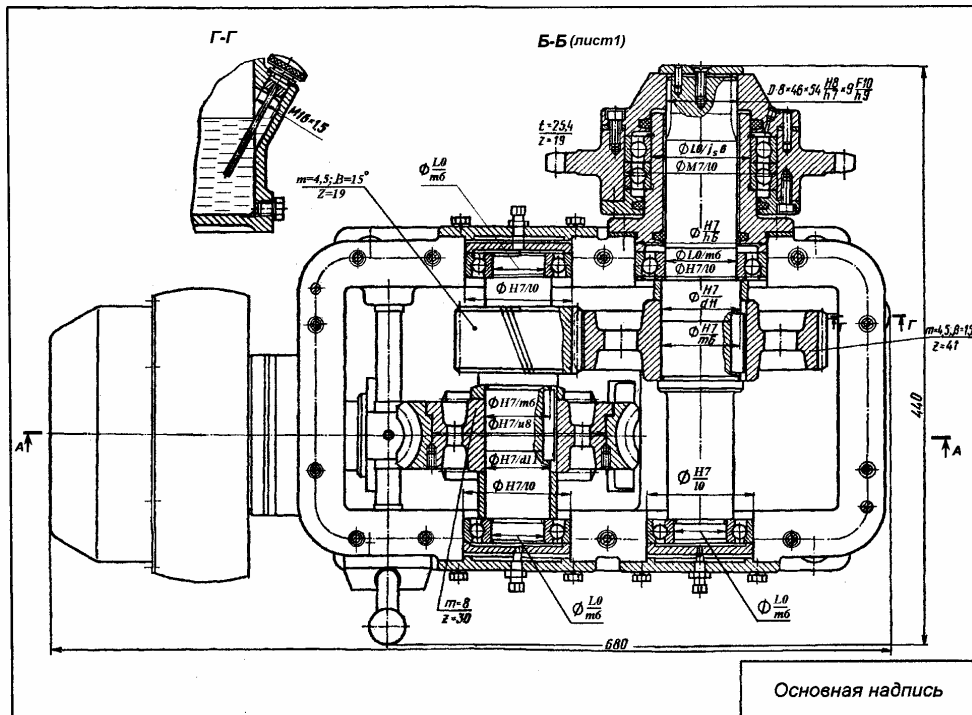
Редуктор червячно-цилиндрический (лист 2)
